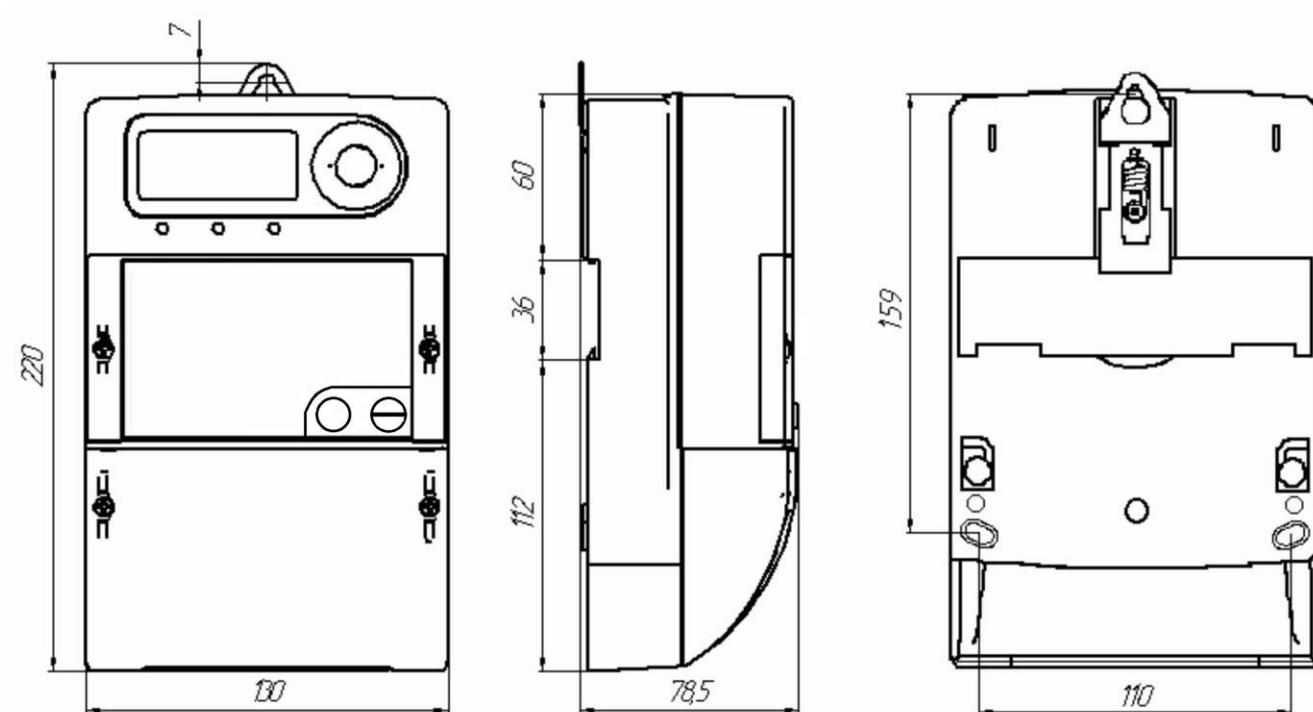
Установочно и габаритные размеры прибора учёта типа TE71 MP-1-3.
